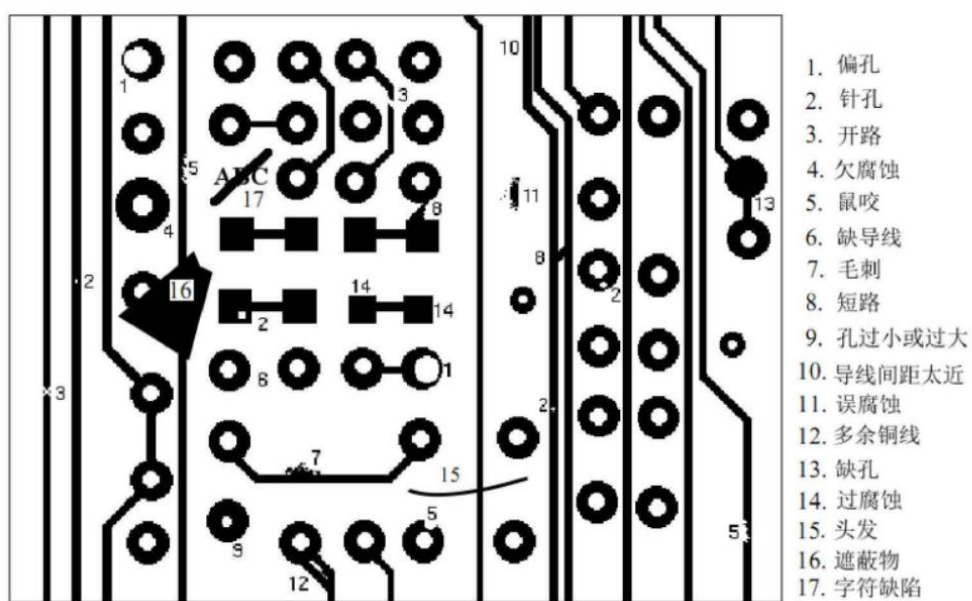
包含多种缺陷的 PCB 示意图
